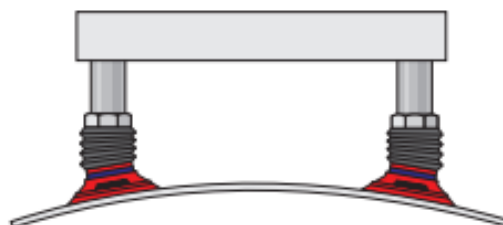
Aplikace přísavky s odpruženým držákem, [2]
